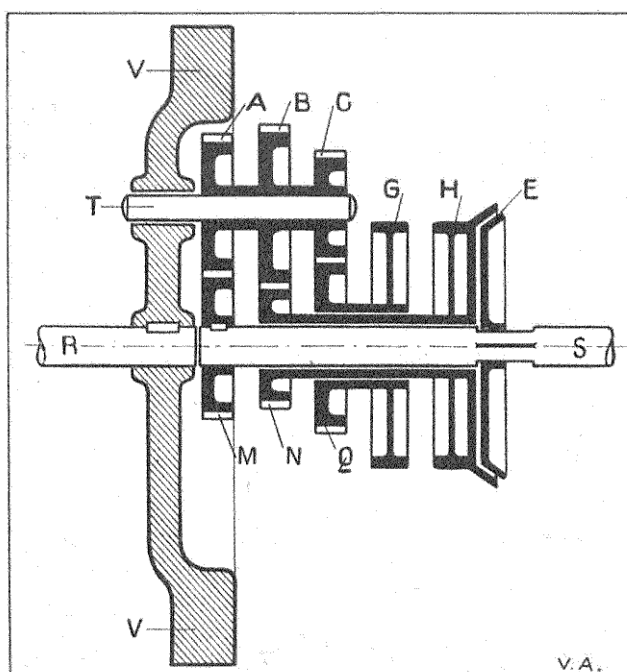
Schéma de construction du changement de vitesse à trains planétaires.
